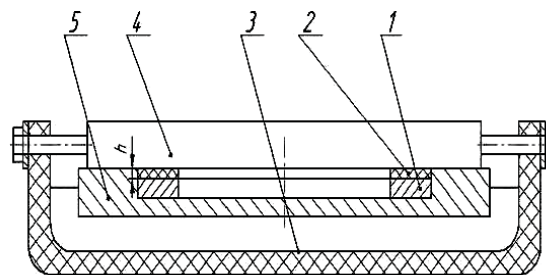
Приспособление для нанесения порошковой композиции: 1 – основание подшипника скольжения; 2 – нанесенная порошковая композиция; 3 – основание; 4 – выравнивающий нож; 5 – матрица
